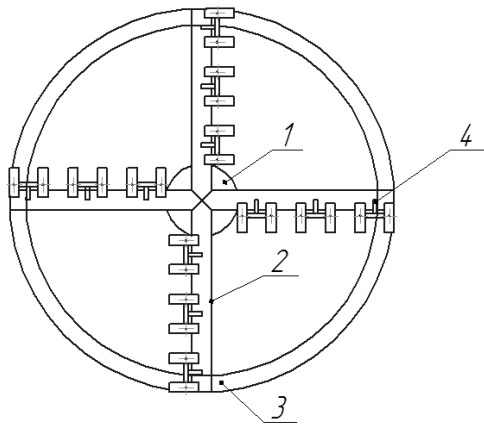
Дисковий робочий орган з клиновидними зубцями
